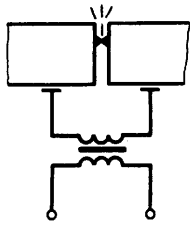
Схема контактной сварки труб оплавлением
